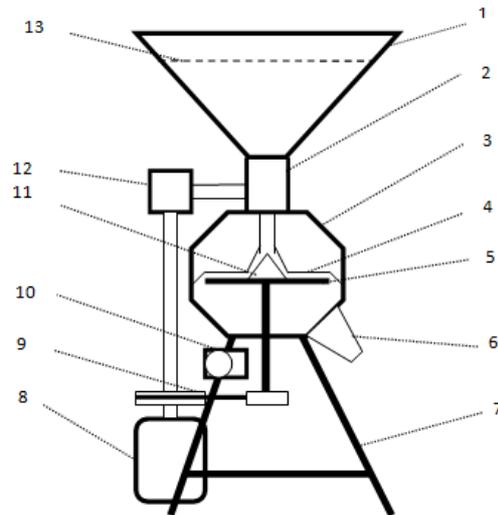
Схема скарификатора: 1 – бункер; 2 – дозирующее устройство; 3 – корпус; 4 – дополнительный диск; 5 – скарифицирующий диск; 6 – выходное отверстие; 7 – рама; 8 – электродвигатель; 9 – клиноремённая передача; 10 – тахометр; 11 – конус; 12 – редуктор; 13 – сетка.
